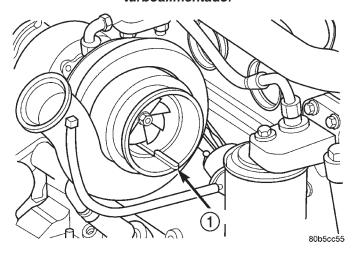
Medición de la holgura radial del cojinete del turboalimentador
